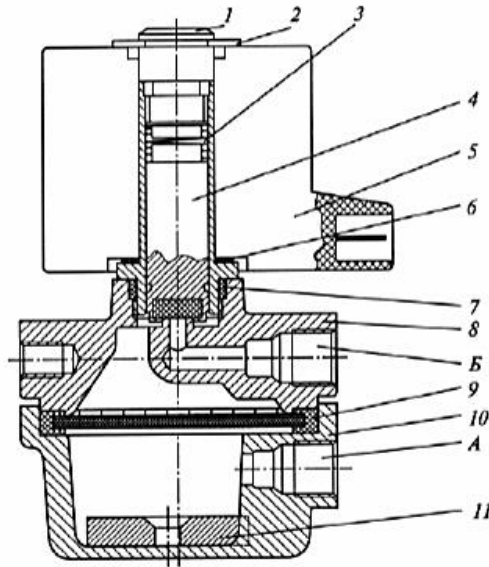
Электромагнитный газовый клапан: 1 - втулка направляющая; 2 - стопорная шайба; 3 - пружина; 4 - якорь; 5 - катушка; 6 - кольцо пружинное; 7 - кольцо уплотнительное; 8 - корпус; 9 - фильтр; 10 - отстойник; 11 - магнит; А - вход газа; Б - выход газа
